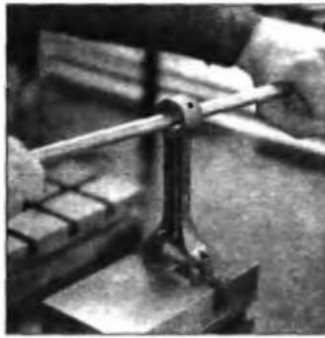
Простой способ правки стержня шатуна при кручении
